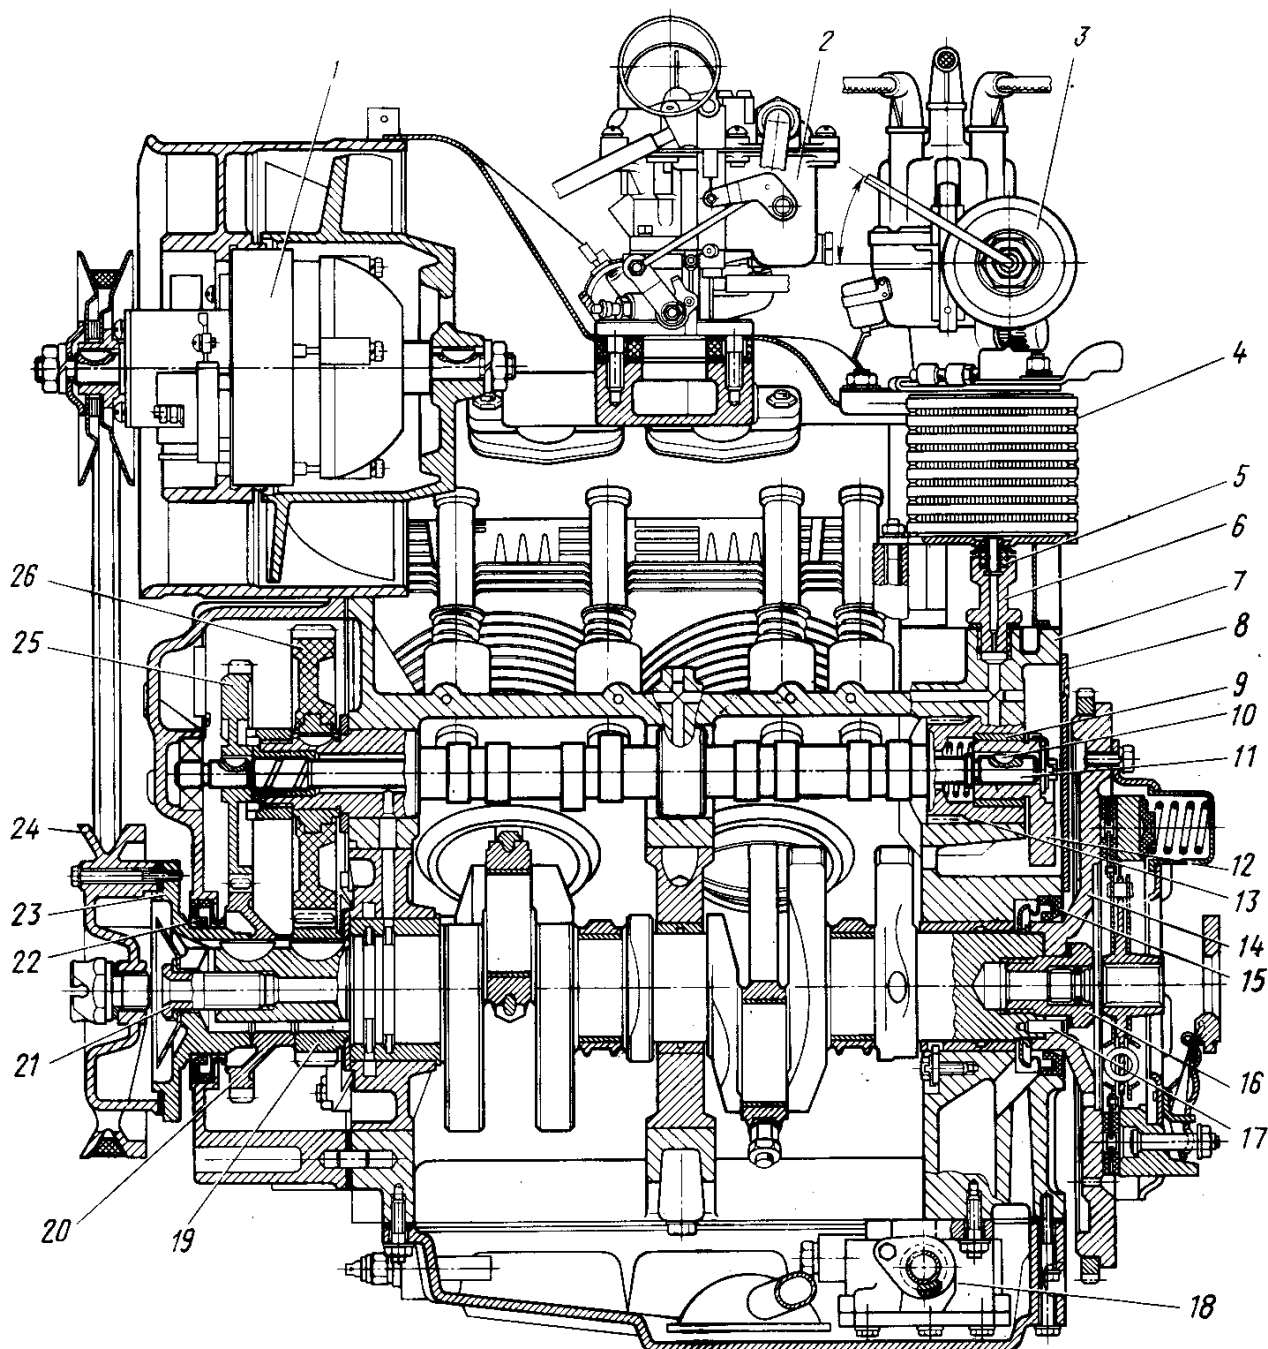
Продольный разрез двигателя: 1 — генератор; 2 — карбюратор; 3 — прерыватель-распределитель; 4 — масляный радиатор; 5 — уплотнитель; 6 — штуцер; 7 — картер коленчатого вала; 8 — крышка; 9 — втулка; 10 — шпонка; 11 — балансирный вал; 12 — противовес; 13 — распределительный вал; 14 — маховик; 15 — задняя манжета коленчатого вала; 16 — болт крепления маховика; 17 — штифт; 18 — масляный насос; 19 — ведущая шестерня привода распределительного вала; 20 — ведущая шестерня привода балансирного вала; 21 — болт крепления корпуса центробежного маслоочистителя; 22 — передняя манжета коленчатого вала; 23 — корпус маслоочистителя; 24 — крышка маслоочистителя; 25 — ведомая шестерня балансирного вала; 26 — ведомая шестерня распределительного вала
